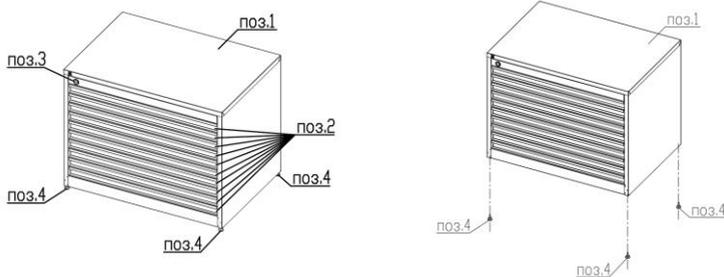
Схема устройства и схема сборки шкафов - драйверов.
